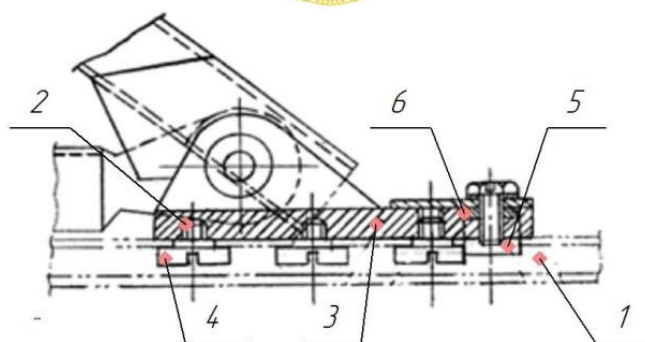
Устройство для крепления оборудования к полу воздушного судна
